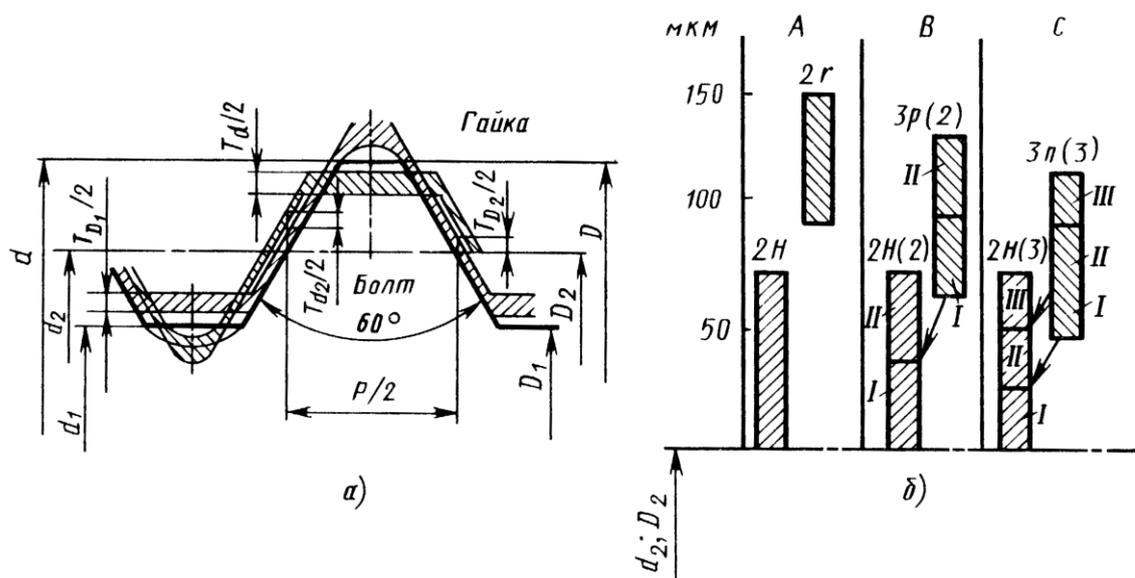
Схемы расположения полей допусков диаметров (а) и среднего диаметра (б) резьбы с натягом
